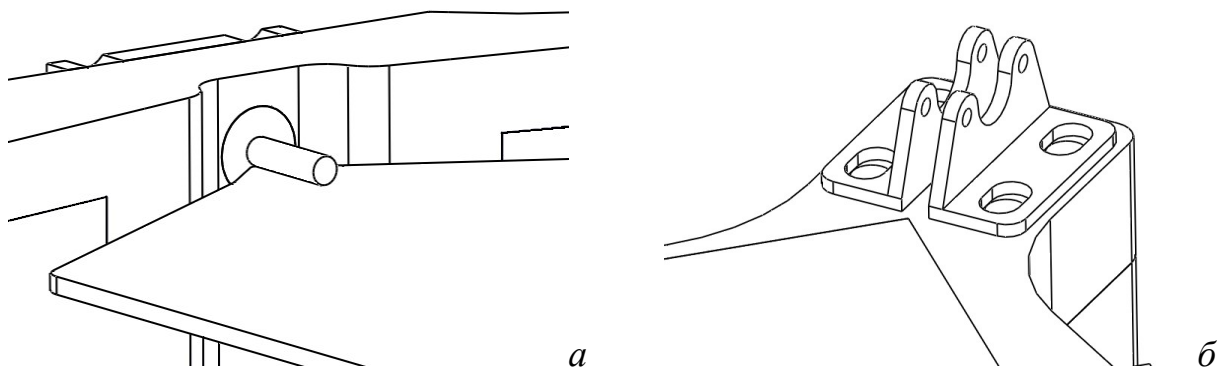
Соединение центрального проводника с СВЧ-соединителем (а),
